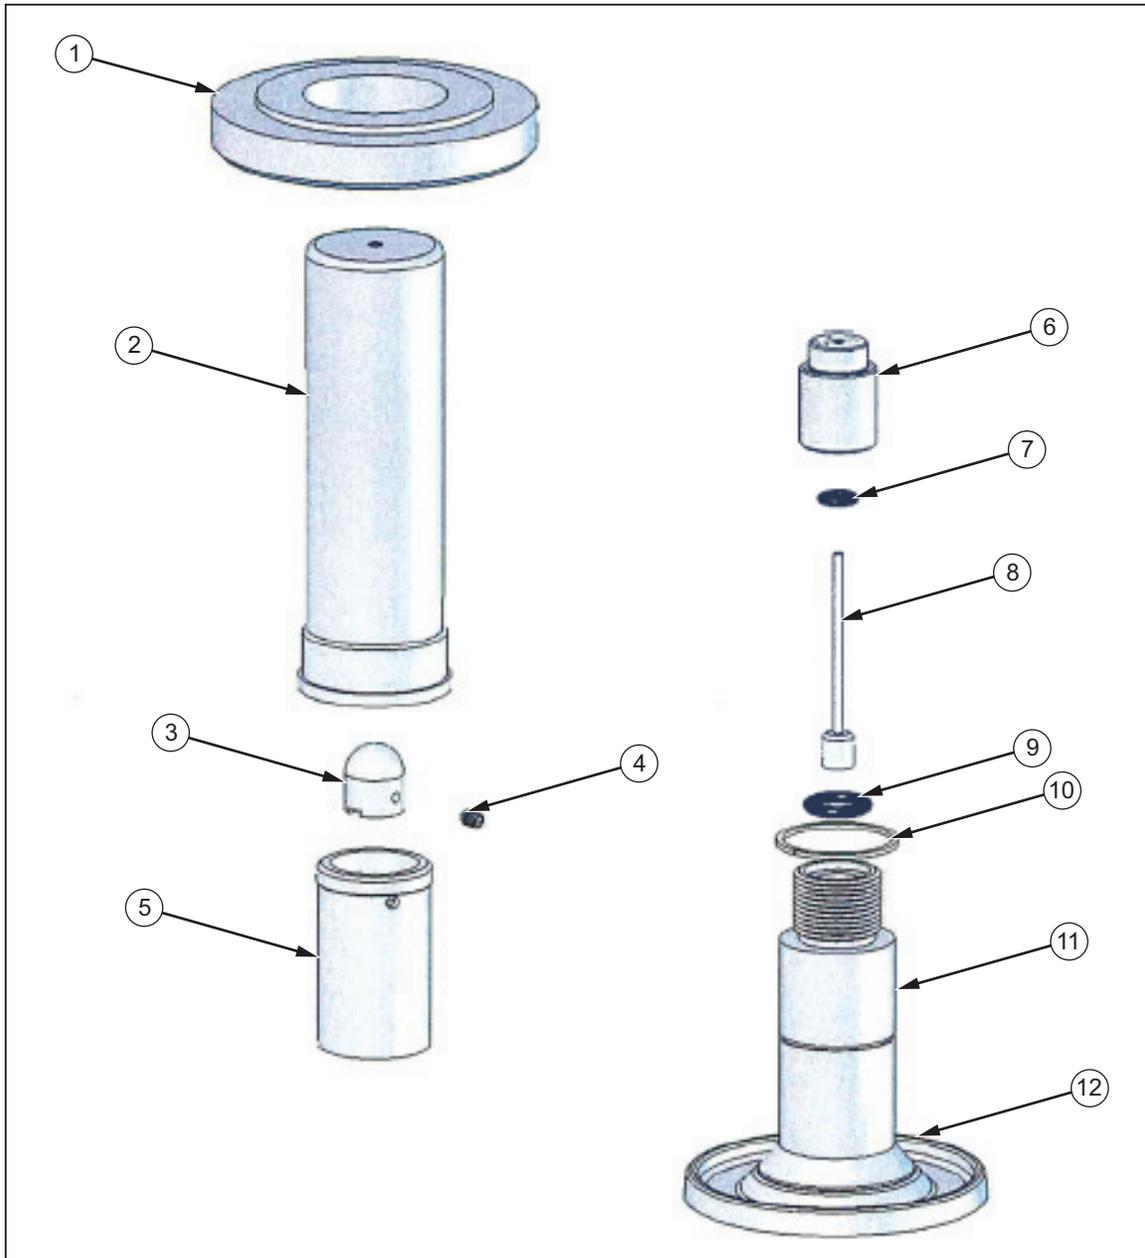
Conjunto de PCU - 2 e 3 mm
